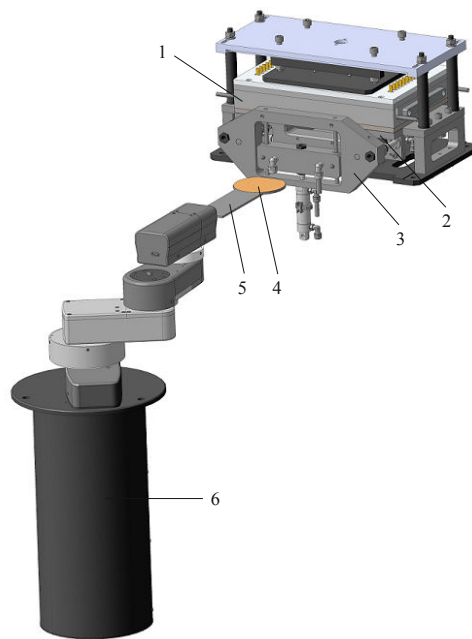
Загрузка полупроводниковой пластины роботизированным комплексом в камеру отжига установки быстрой термообработки: 1 – блок нагрева, 2 – камера отжига, 3 – затвор, 4 – полупроводниковая пластина, 5 – подложкодержатель, 6 – робот-манипулятор
